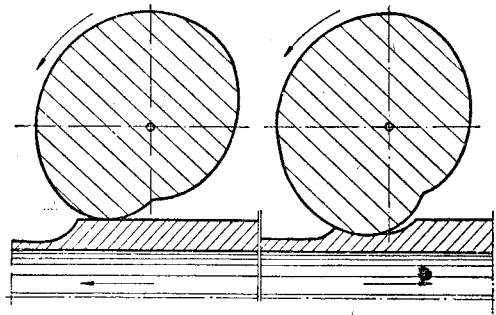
Взаимное расположение заготовки и валков перед захватом и после захвата заготовки валками пилигримового стана.
